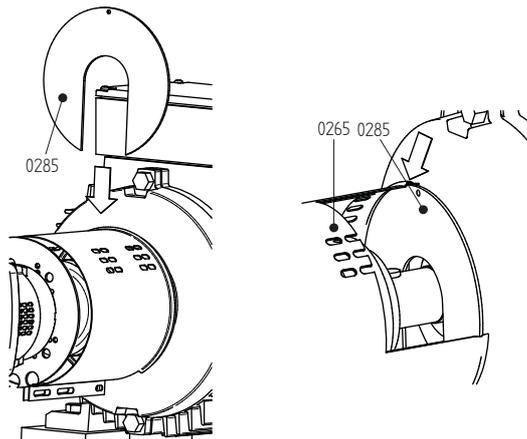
Montieren der Montageplatte auf der Motorseite.
